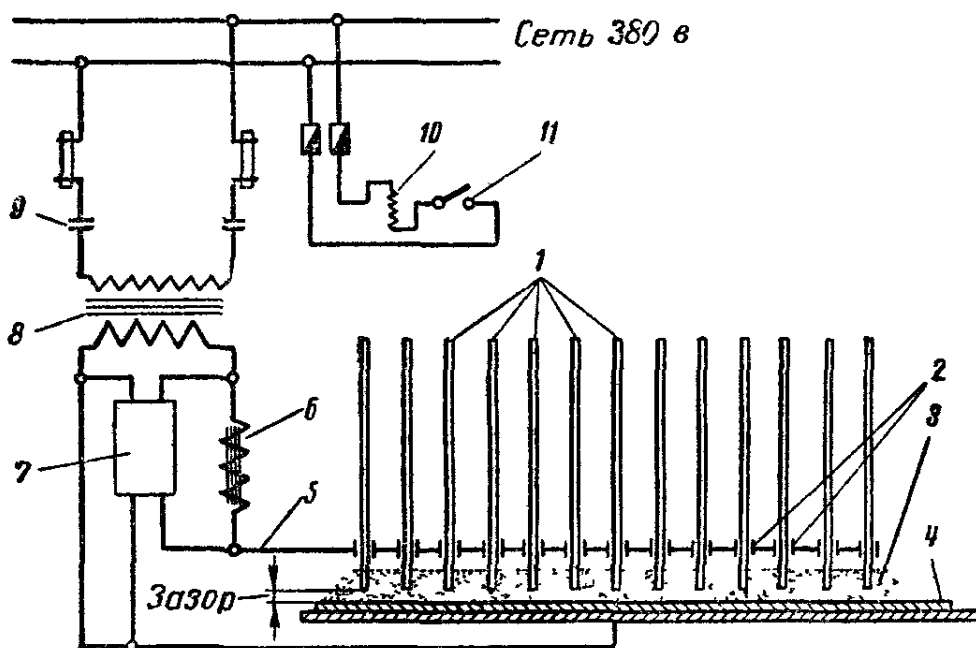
Схема многоточечной автоматической сварки под флюсом
